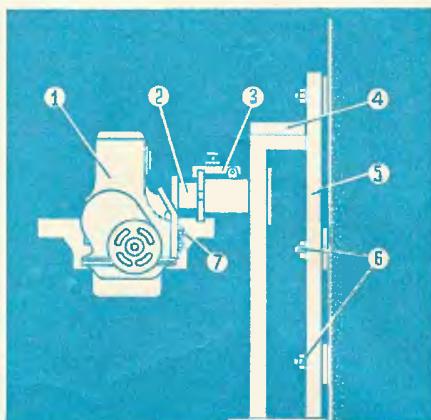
Стенд для разборки и сборки коробки передач автомобилей ЗИЛ и ГАЗ: 1 — коробка передач; 2 — поворотный стол; 3 — стойка (труба диаметром 100 мм); 4 — кронштейн для крепления стендса к стене (швеллер № 12); 5 — полка для инструмента; 6 — шарнир; 7 — откидная площадка; 8 — болты для крепления коробки передач; 9 — болты для крепления стендса к стене.
